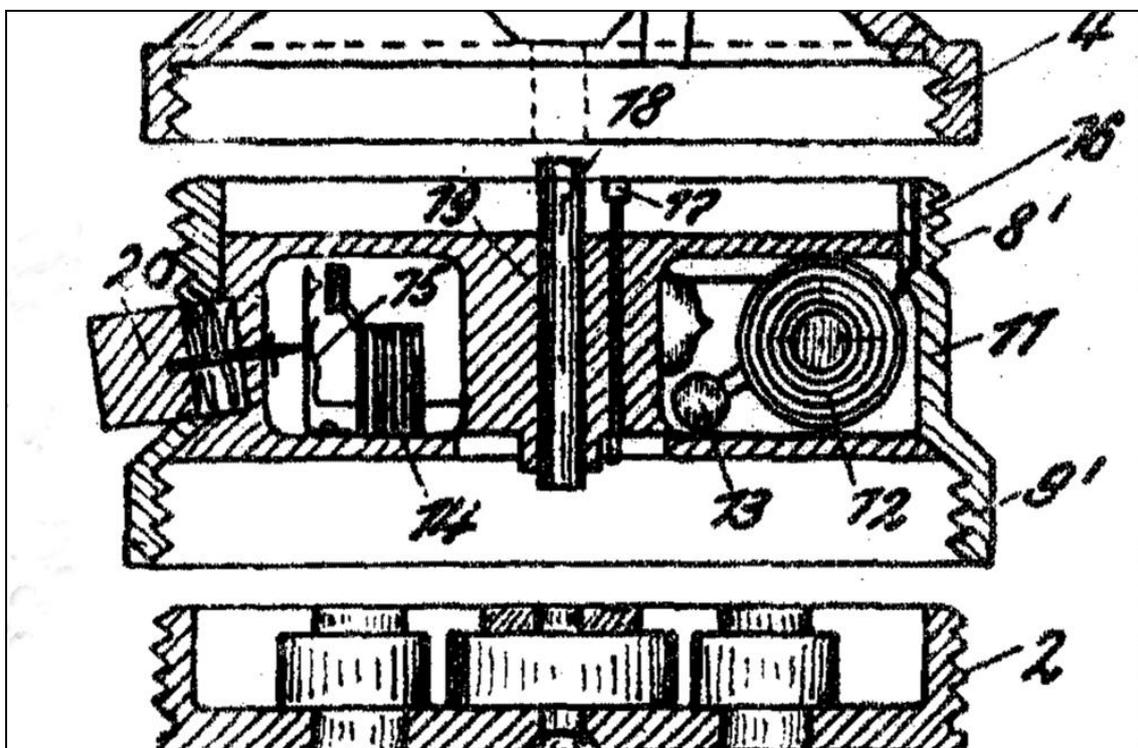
Detalle del aparato (Arch. J.M. Sanchis)
